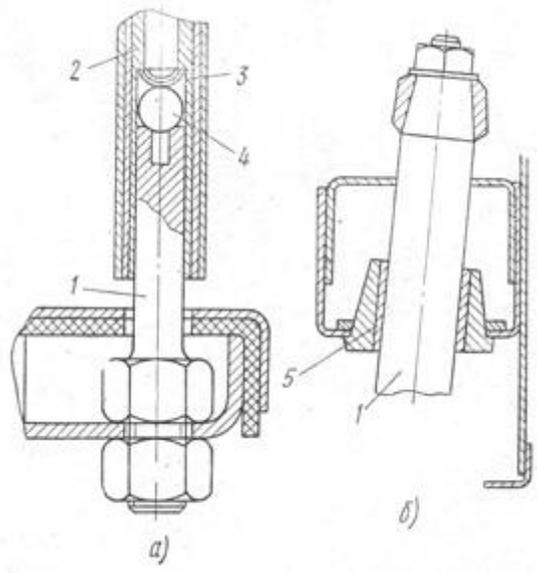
Крепление створок троллейбусов ЗИУ-5Д и ЗИУ-9.
